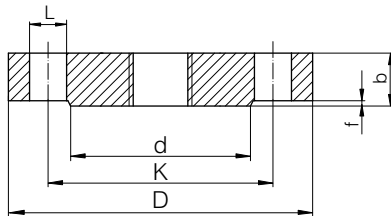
Encombrement - bride DIN DIN 2501 (portée de joint DIN 2526 forme C)
